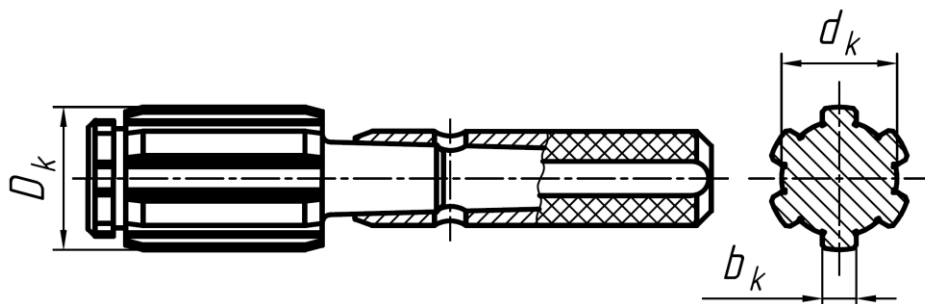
Прохідний шліцьовий калібр-пробка
